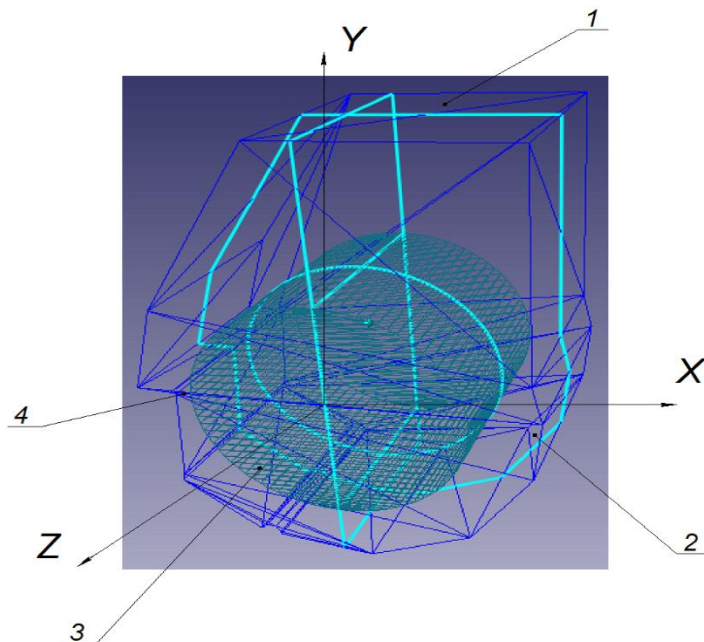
Модель безлопатевої дискретної тістомісильної машини: 1 – горловина завантаження; 2 – корпус робочої камери; 3 – безлопатевий робочий орган; 4 – пасивний вібраційний пристрій (ПВП)
